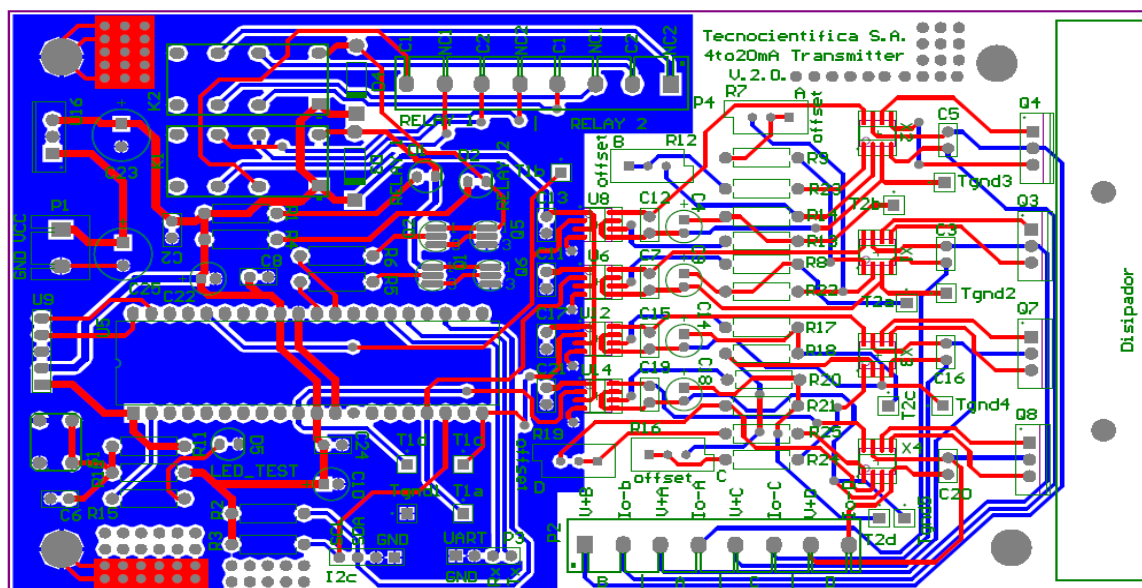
Top Layer - PCB Transmisor de 4 a 20mA.
